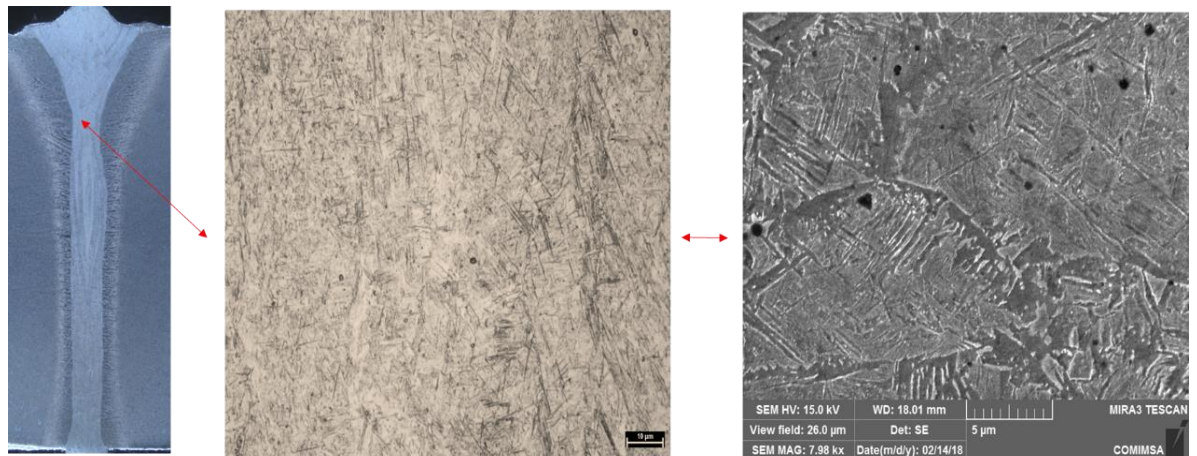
vista microscópica de la parte superior de la soldadura.
